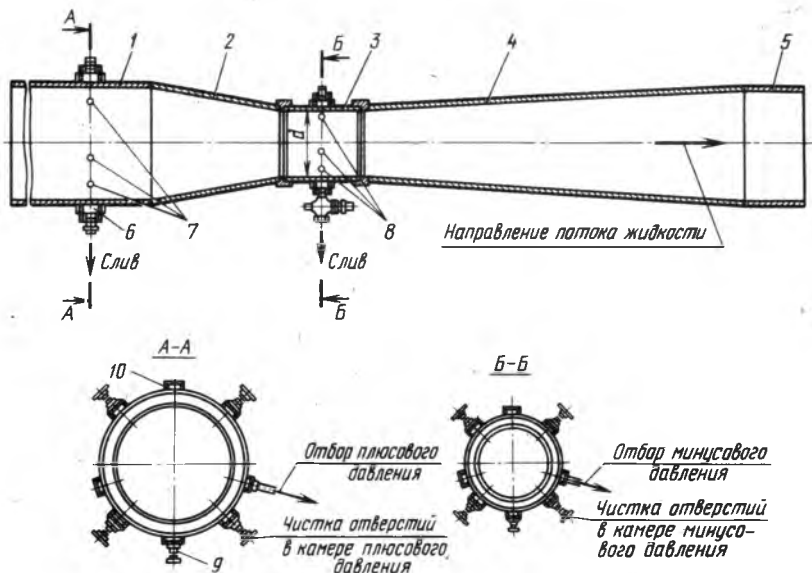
Общий вид сварной трубы Вентури:
